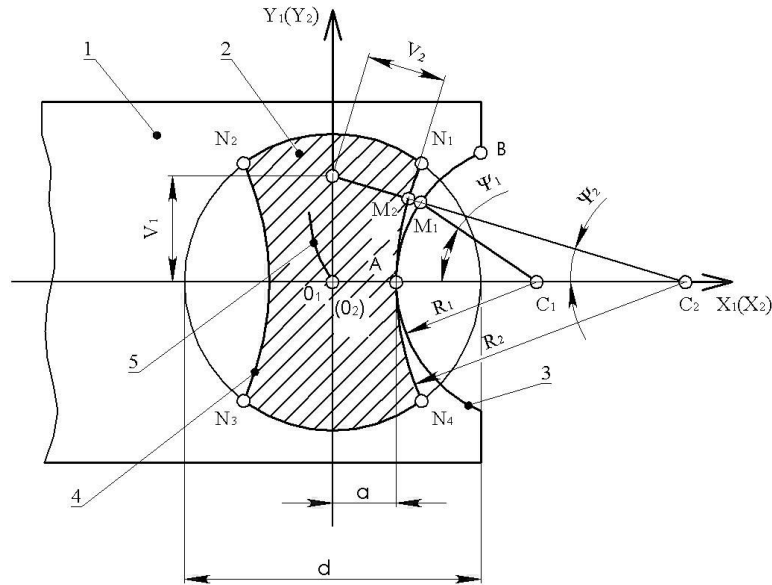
Початкове положення деталей шарніра кочення: 1 – пластина; 2 – валик; 3 – опукла робоча поверхня отвору пластини; 4 – увігнута робоча поверхня валика; 5 – траєкторія руху центру валика
